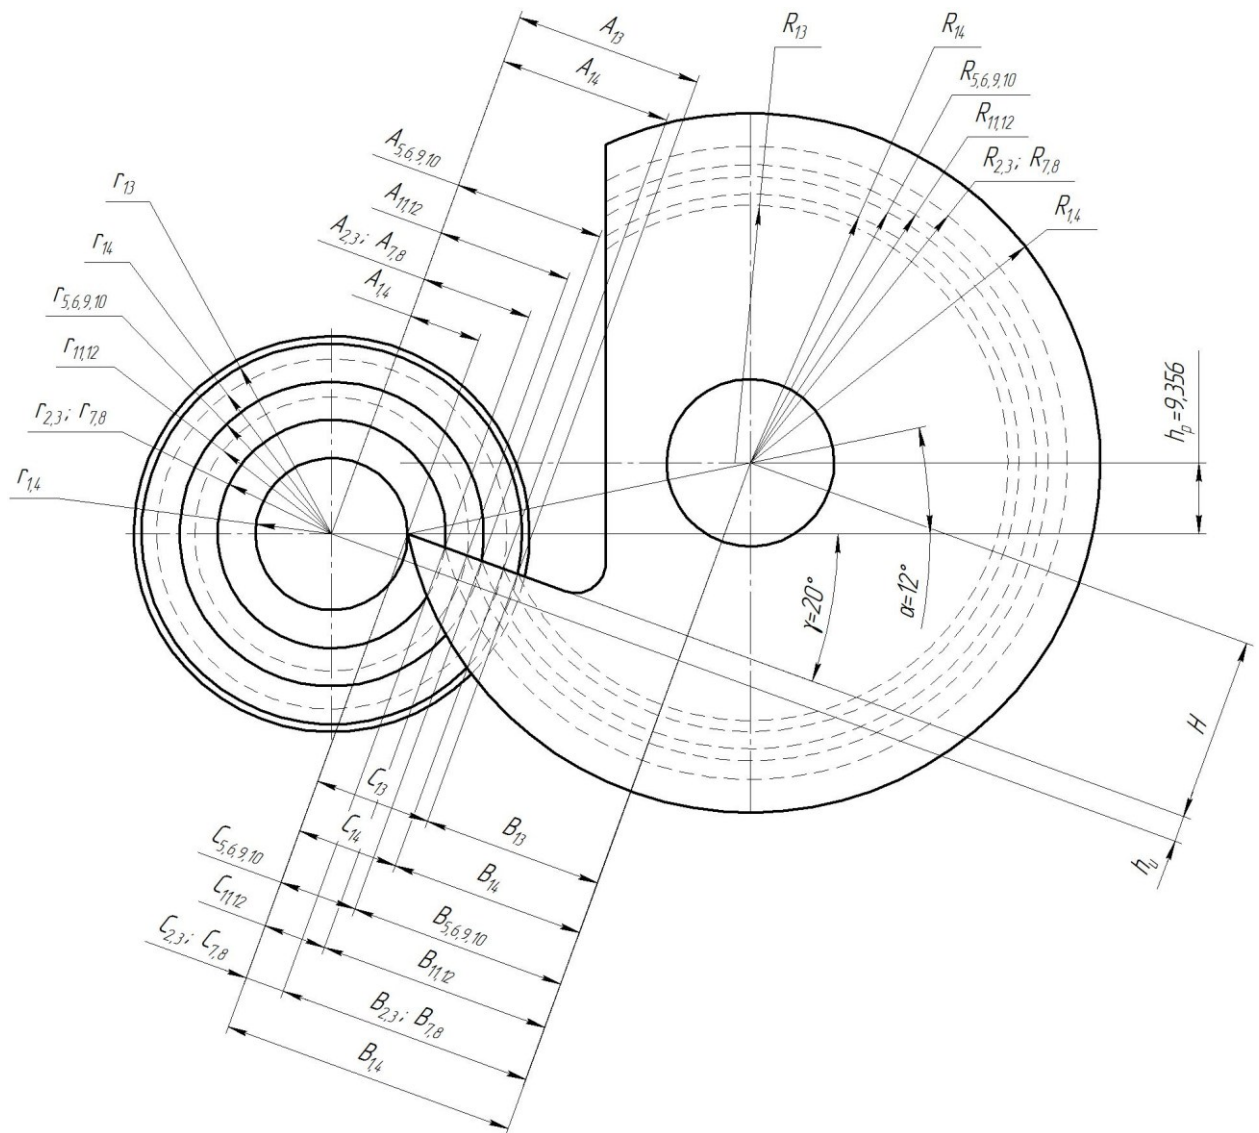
Схема для розрахунку круглого фасонного різця.
